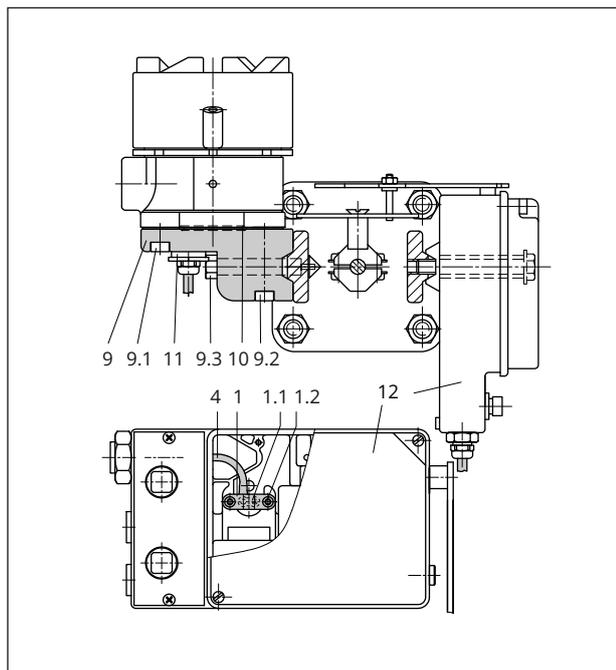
NAMUR-Anbau an Stellventil mit Stellungsregler Typ 4765
